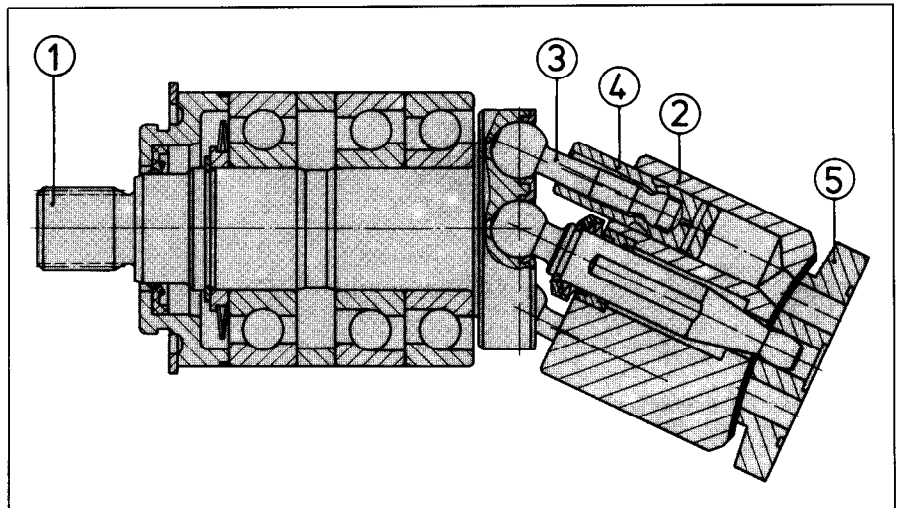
Prinzipskizze einer Axialkolbenmaschine in Schrägachsenbauart
